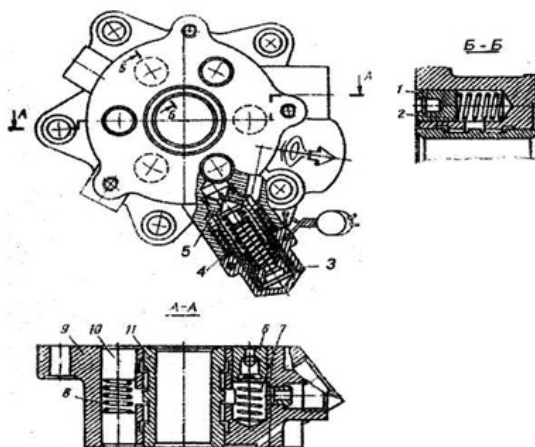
Распределитель гидравлического усилителя: 1,20-плунжеры; 2,7,8 - пружины; 3 - колпак клапана; 4 - прокладка; 5,6 - клапаны;9-корпус; 11 - золотник.
